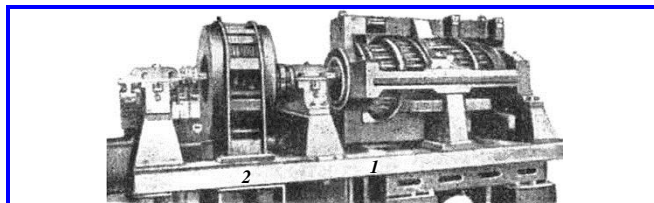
Общий вид униполярного генератора для электросварки фирмы Westinghouse Electric Corporation на 150 кА, 7,5 В: 1 – генератор; 2 – приводной электродвигатель
